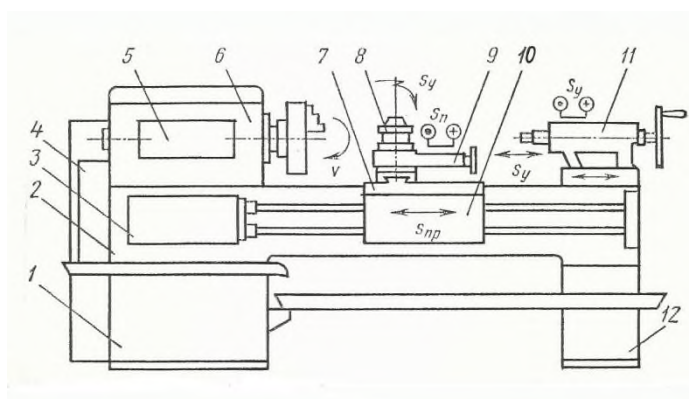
Общий вид токарно-винторезного станка 16К20
